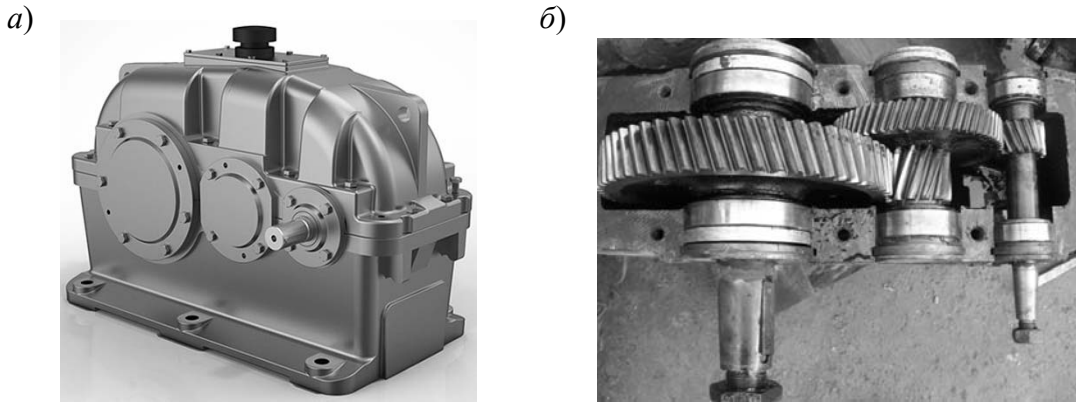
Общий вид двухступенчатого цилиндрического редуктора в корпусе (а) и со снятой крышкой (б)
